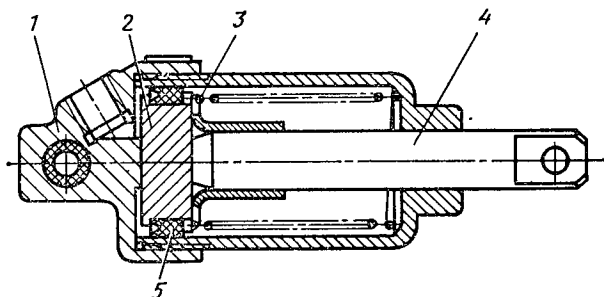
Пневмоцилиндр привода рычага остановки двигателя:
